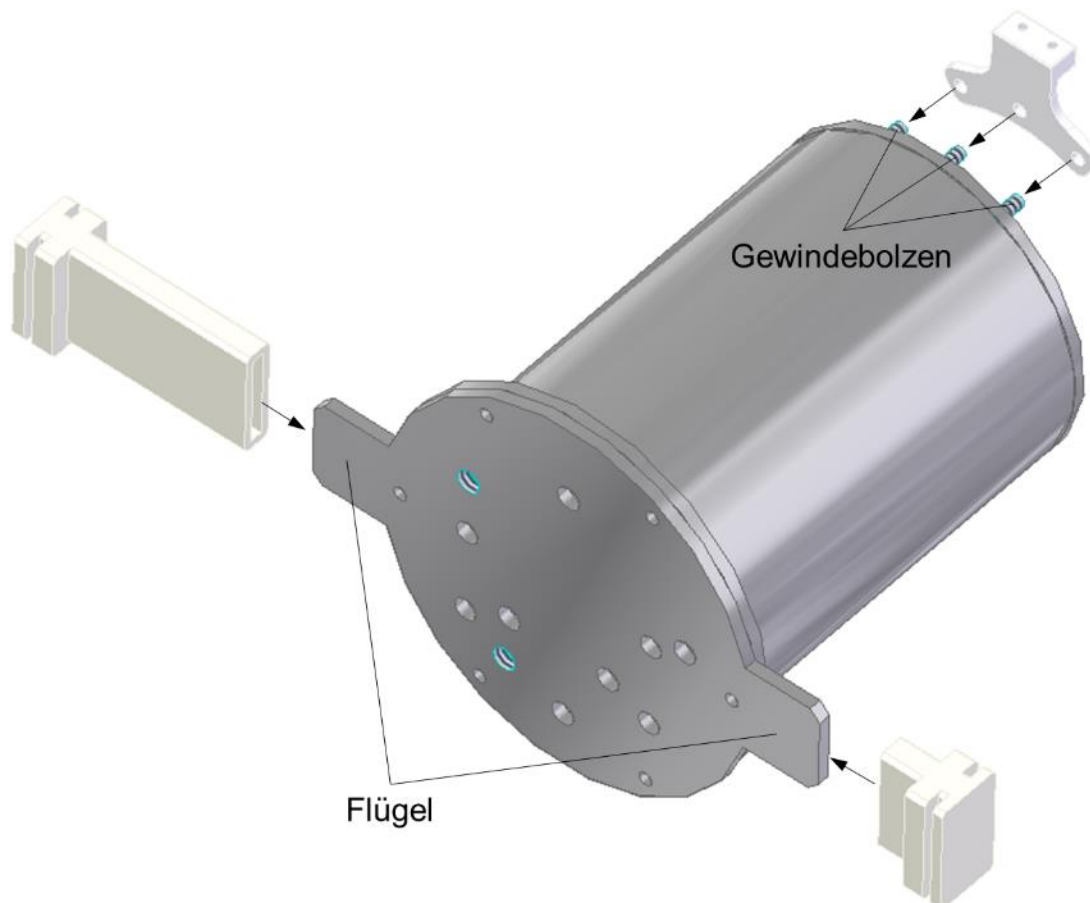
Schnittstellen Boiler - Grundrahmen
